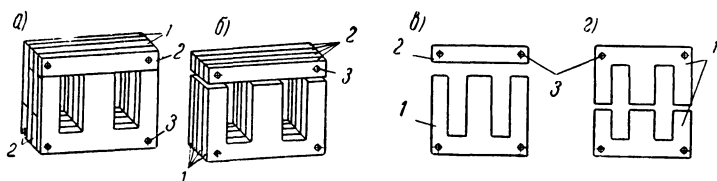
Виды штампованных пластин сердечников и их сборки: а, б — пластины с нормальным ярмом; в, г — пластины с уширенным ярмом; а — сборка вперекрышку; б — сборка в стык; в — разъем по ярму; г — разъем по стержню.
